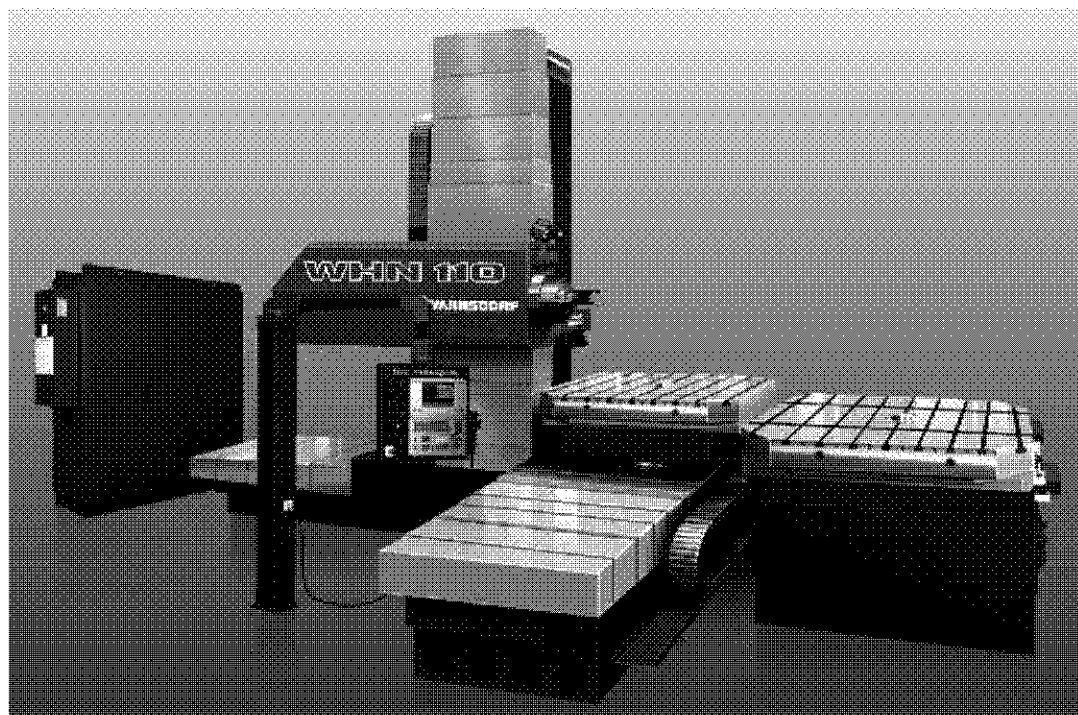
Горизонтально-расточной обрабатывающий центр с ЧПУ WHN110Q
